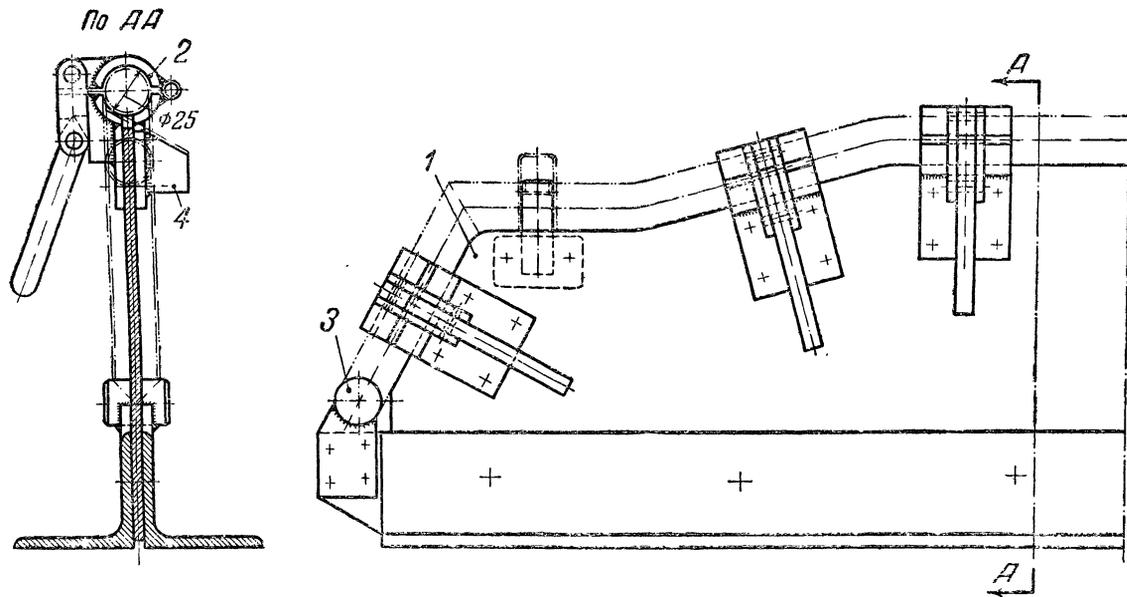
Приспособление для правки каркаса люка местным нагревом.
